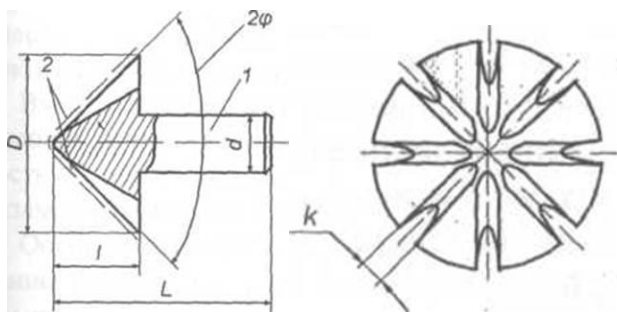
конструкція одношарової алмазної конічної зенківки: 1 – корпус зенківки; 2 – алмазовмісний робочий шар.
